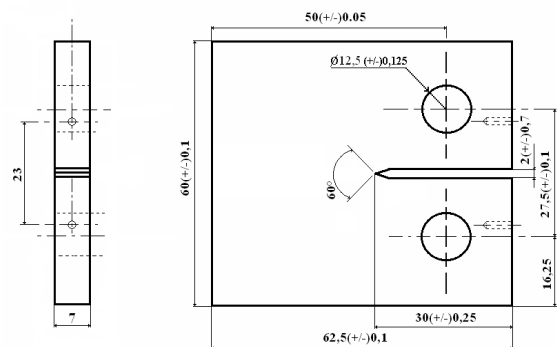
Éprouvette CT50 utilisé pour les essais de fissuration
